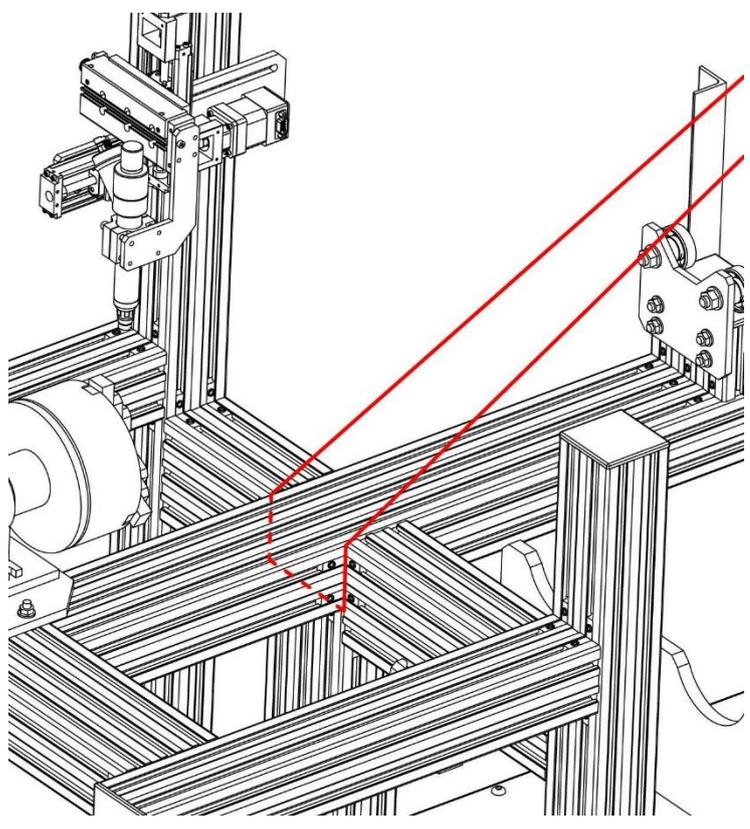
Строповка со стороны левой сварочной головки
